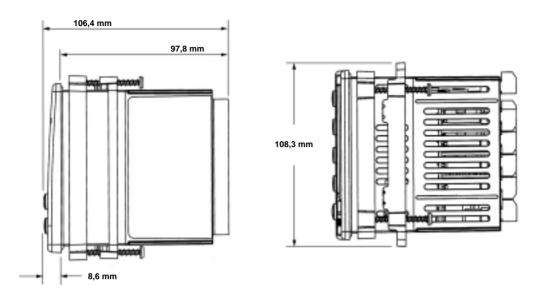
Vue latérale, vue de dessus et dimensions.
